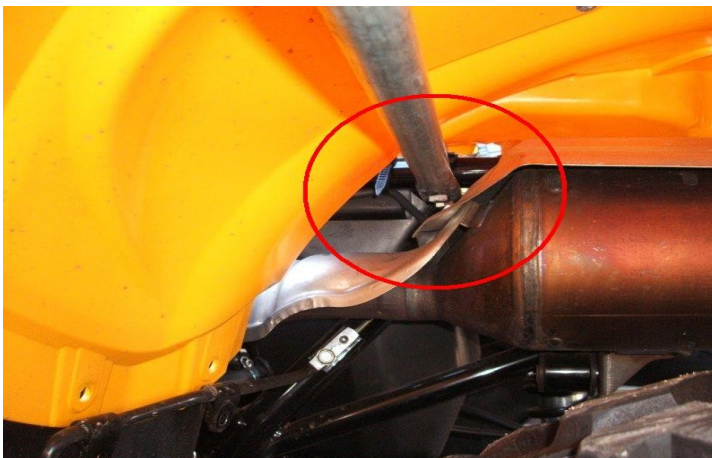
Detalhe, visto por baixo, do local de fixação do tirante inferior dianteiro.
